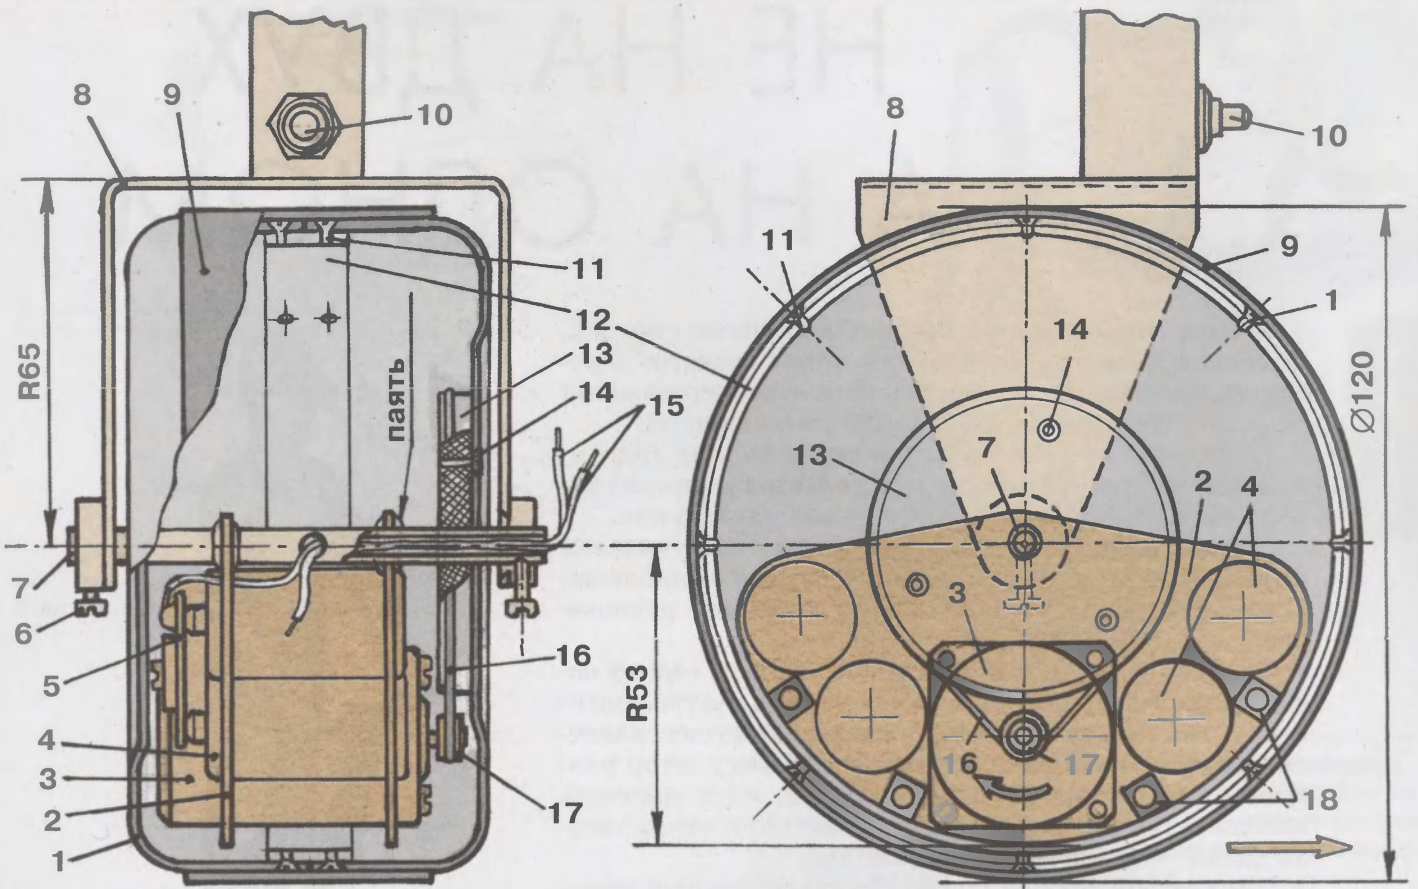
Устройство одноколесной модели самоката: 1 — колесо; 2 — рама; 3 — электромотор; 4 — батареи питания; 5 — токосъемные клеммы; 6 — стопорный винт; 7 — ось; 8 — платформа самокатчика; 9 — резиновое кольцо колеса; 10 — выключатель; 11 — крепление деталей колеса; 12 — соединительное кольцо; 13 — большой шкив; 14 — крепление шкива к колесу; 15 — провода выключателя модели; 16 — пассик; 17 — ведущий (малый) шкив; 18 — свинцовые соединительные втулки.
